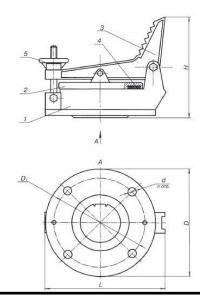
Световой люк ЛС-500. Изображение (слева) и общий вид (справа), [14]: 1 — крышка; 2 — прокладка; 3 — корпус; 4 — гайка; 5 — болт; 6 — усиливающая накладка.
